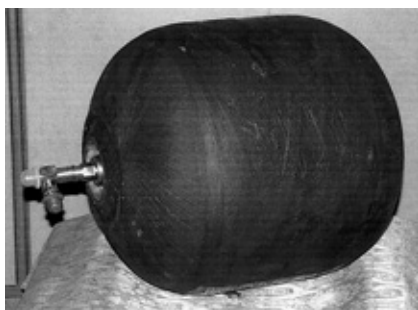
Опытный металлокомпозитный баллон высокого давления
